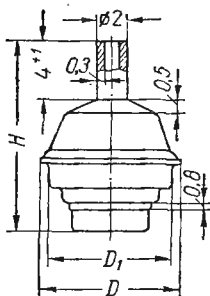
Внешний вид и габаритные размеры изоляторов типа ИКПТ (0,6—5 кв).
